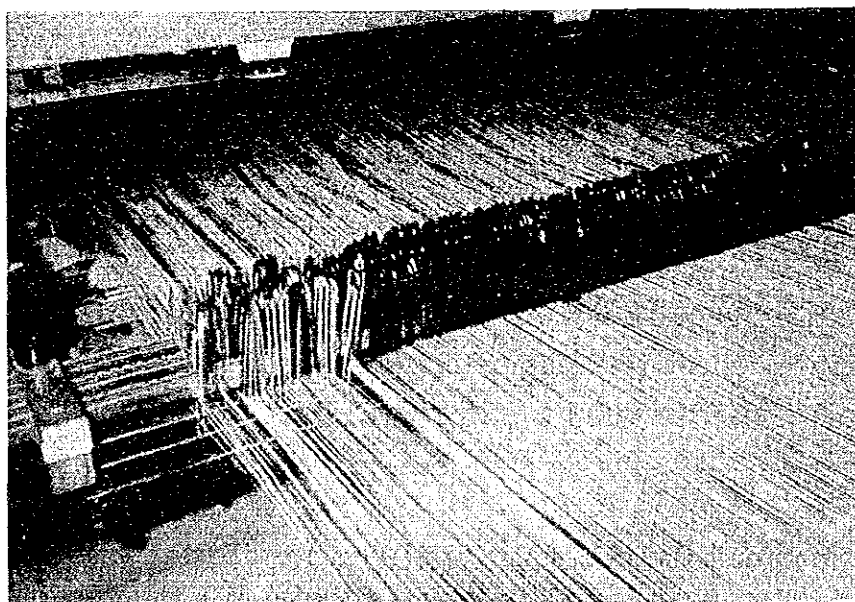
紡績糸に毛羽、Nep、Slubが極めて多く
